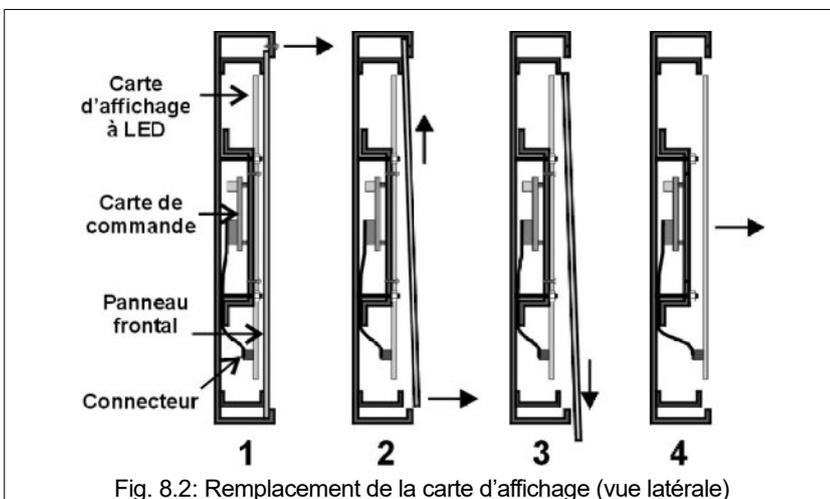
Remplacement de la carte d'affichage (vue latérale)
